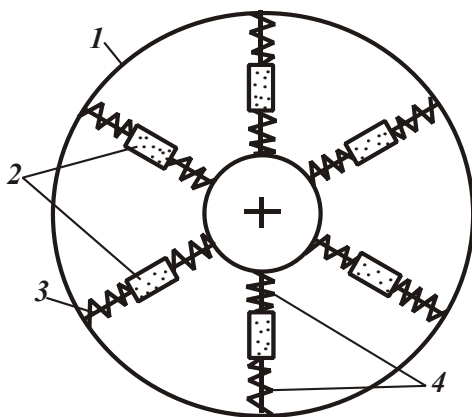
Инструмент для совместной обкатки и шлифования: 1 - корпус; 2 - круг-ролик; 3 - ось, на которой вращается круг; 4 - пружины.
